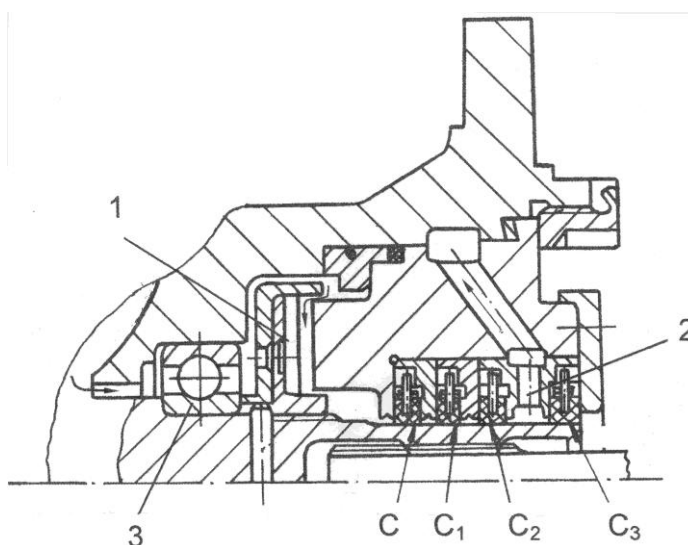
Уплотнение опоры ротора агрегата подачи топлива двигателя НК–361
